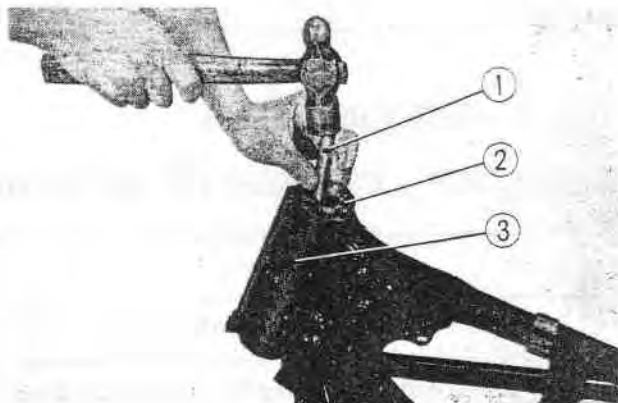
① Jet en bois ③ Tube de direction
